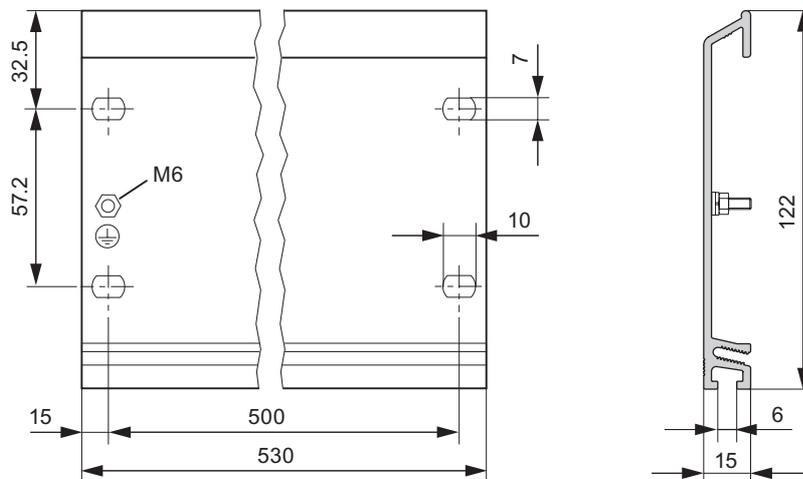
标准宽度为 530 mm 的固定导轨的尺寸图。
